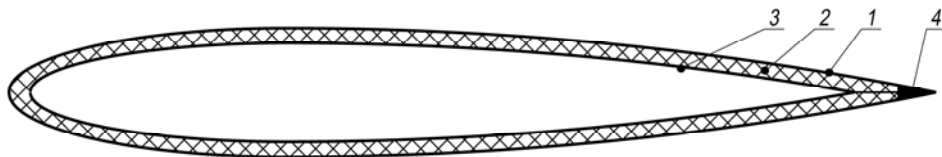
Сечение стабилизатора (1): 1 – обшивка, 2 – наполнитель, 3 – вкладыш, 4 – хвостовой стрингер
